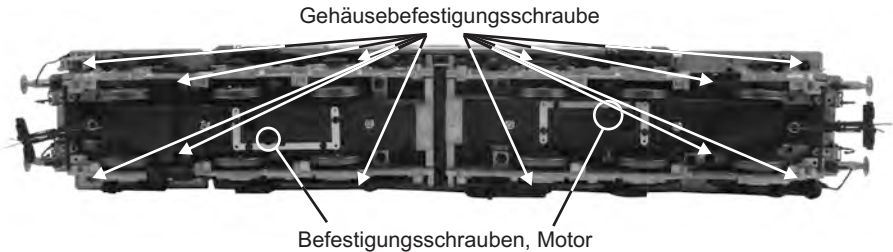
Einbaulage der Befestigungsschrauben von Gehäuse und Motor
